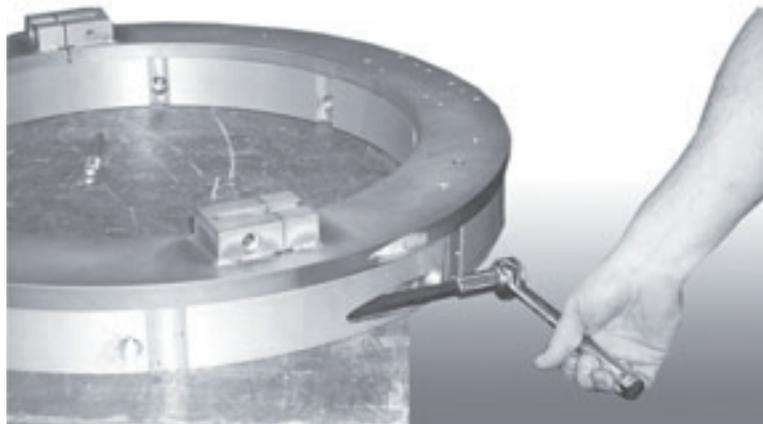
Assemblare le due metà dell'anello e serrare i prigionieri.
